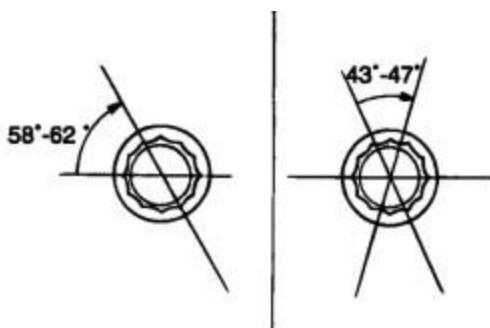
Схема доворота болтов крепления головки блока цилиндров
